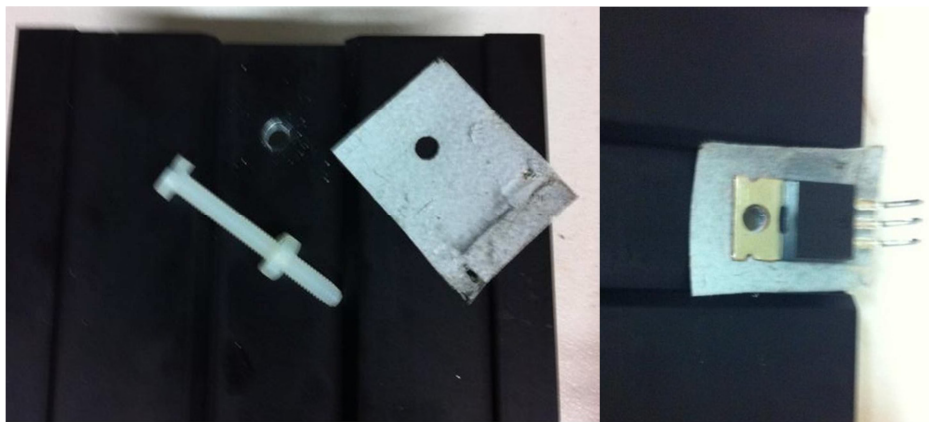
Assemblaggio Dissipatore Mosfet
